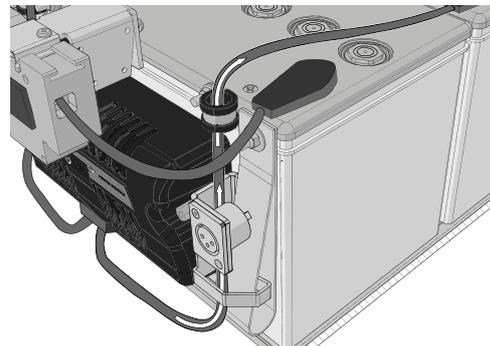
Conecte el cable que está conectado a la terminal delantera derecha de la batería en su soporte de cable como se muestra.
